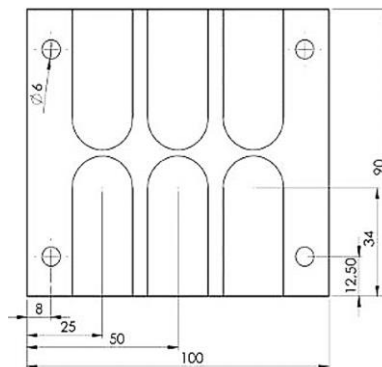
Desenho do corpo de prova com as dimensões após a usinagem.
